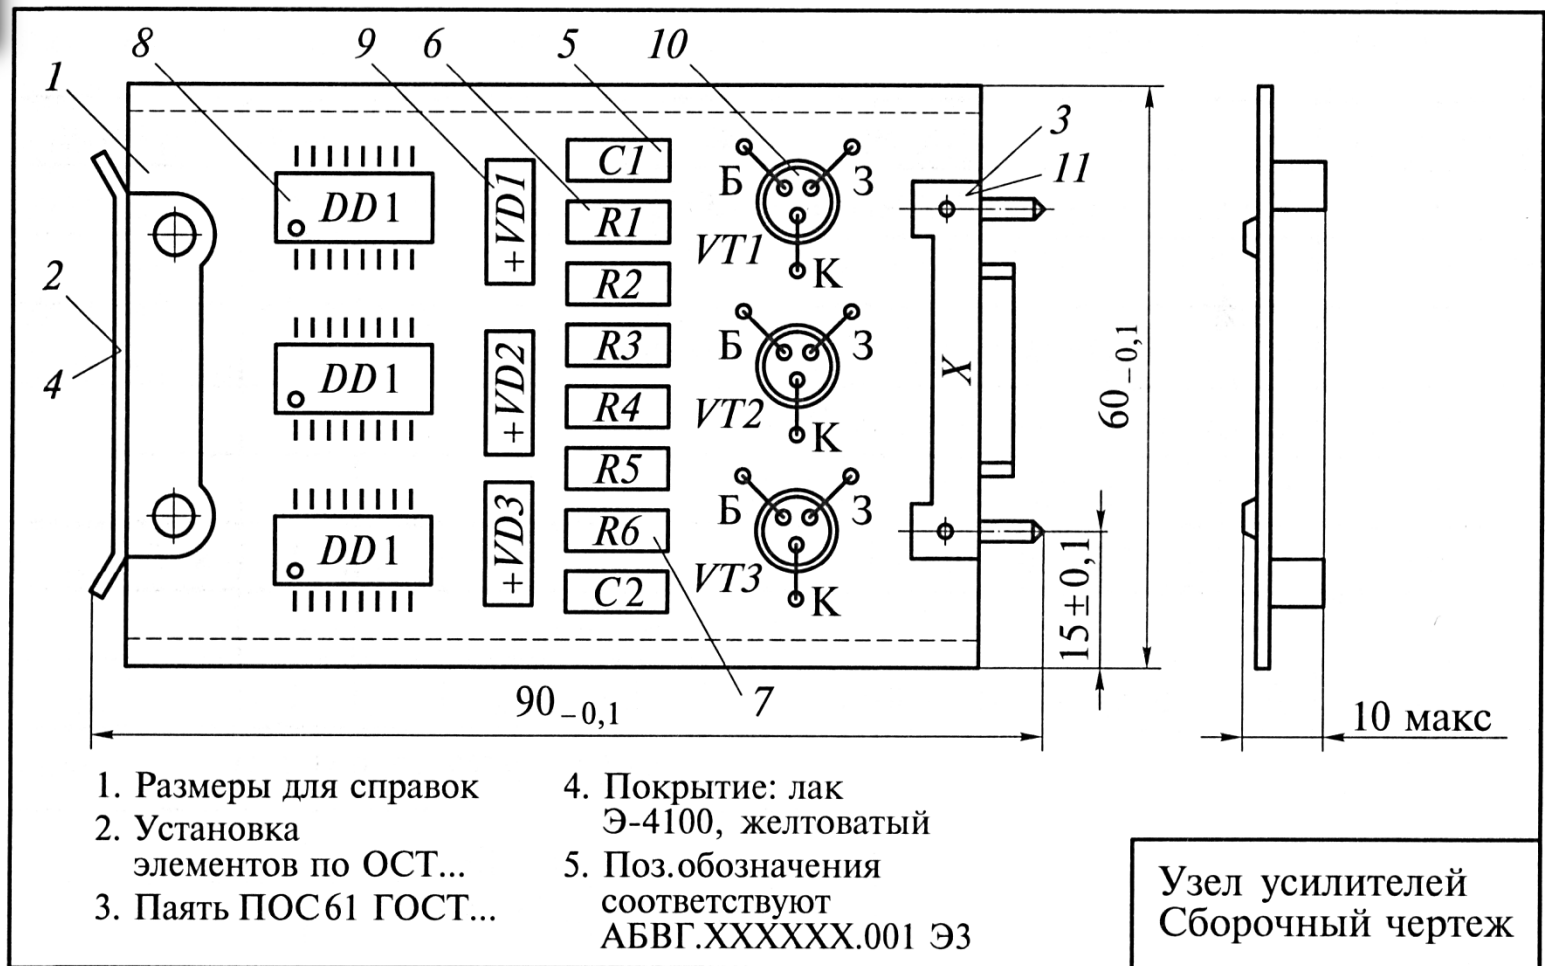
Фрагмент сборочного чертежа узла усилителей
